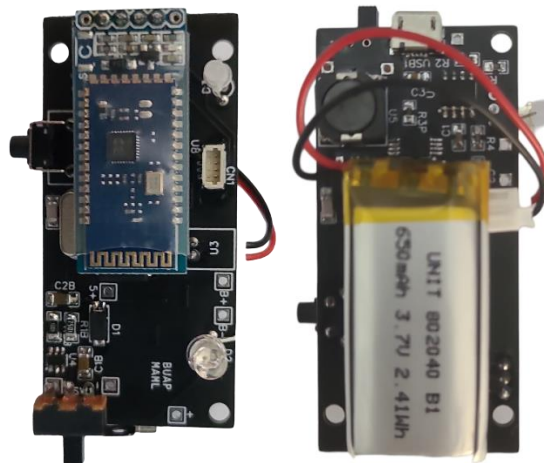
PCB con los componentes necesarios. a) Vista superior b) Vista inferior.
